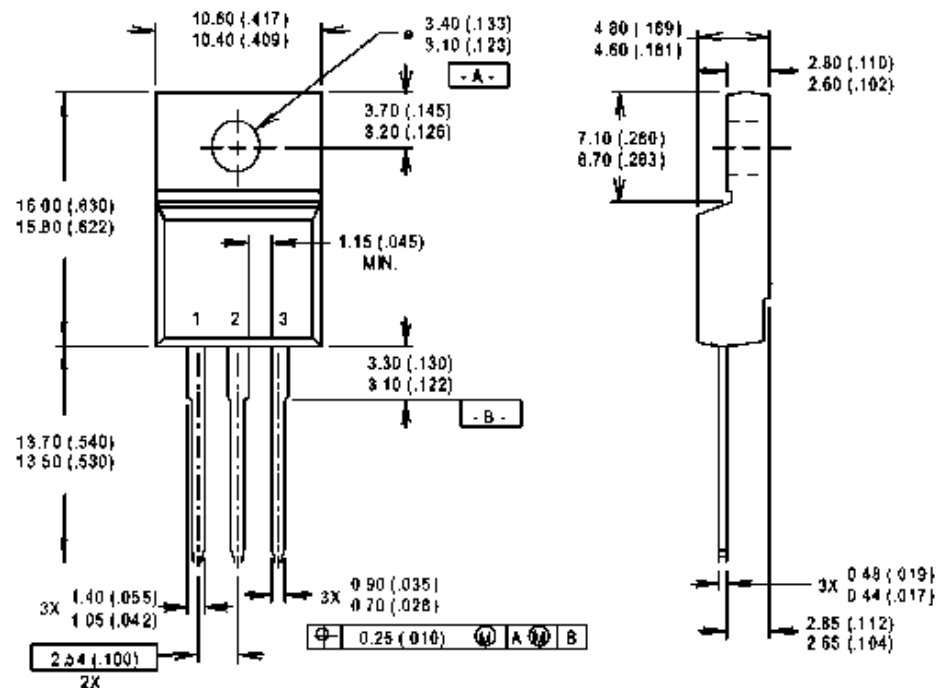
Габаритні розміри транзистора 2N5319
